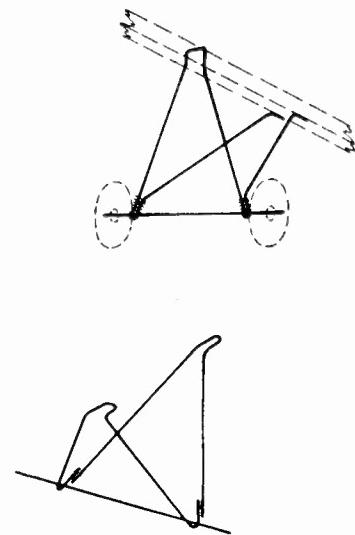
Normale Fahrwerksbauweisen, Stahldraht.
